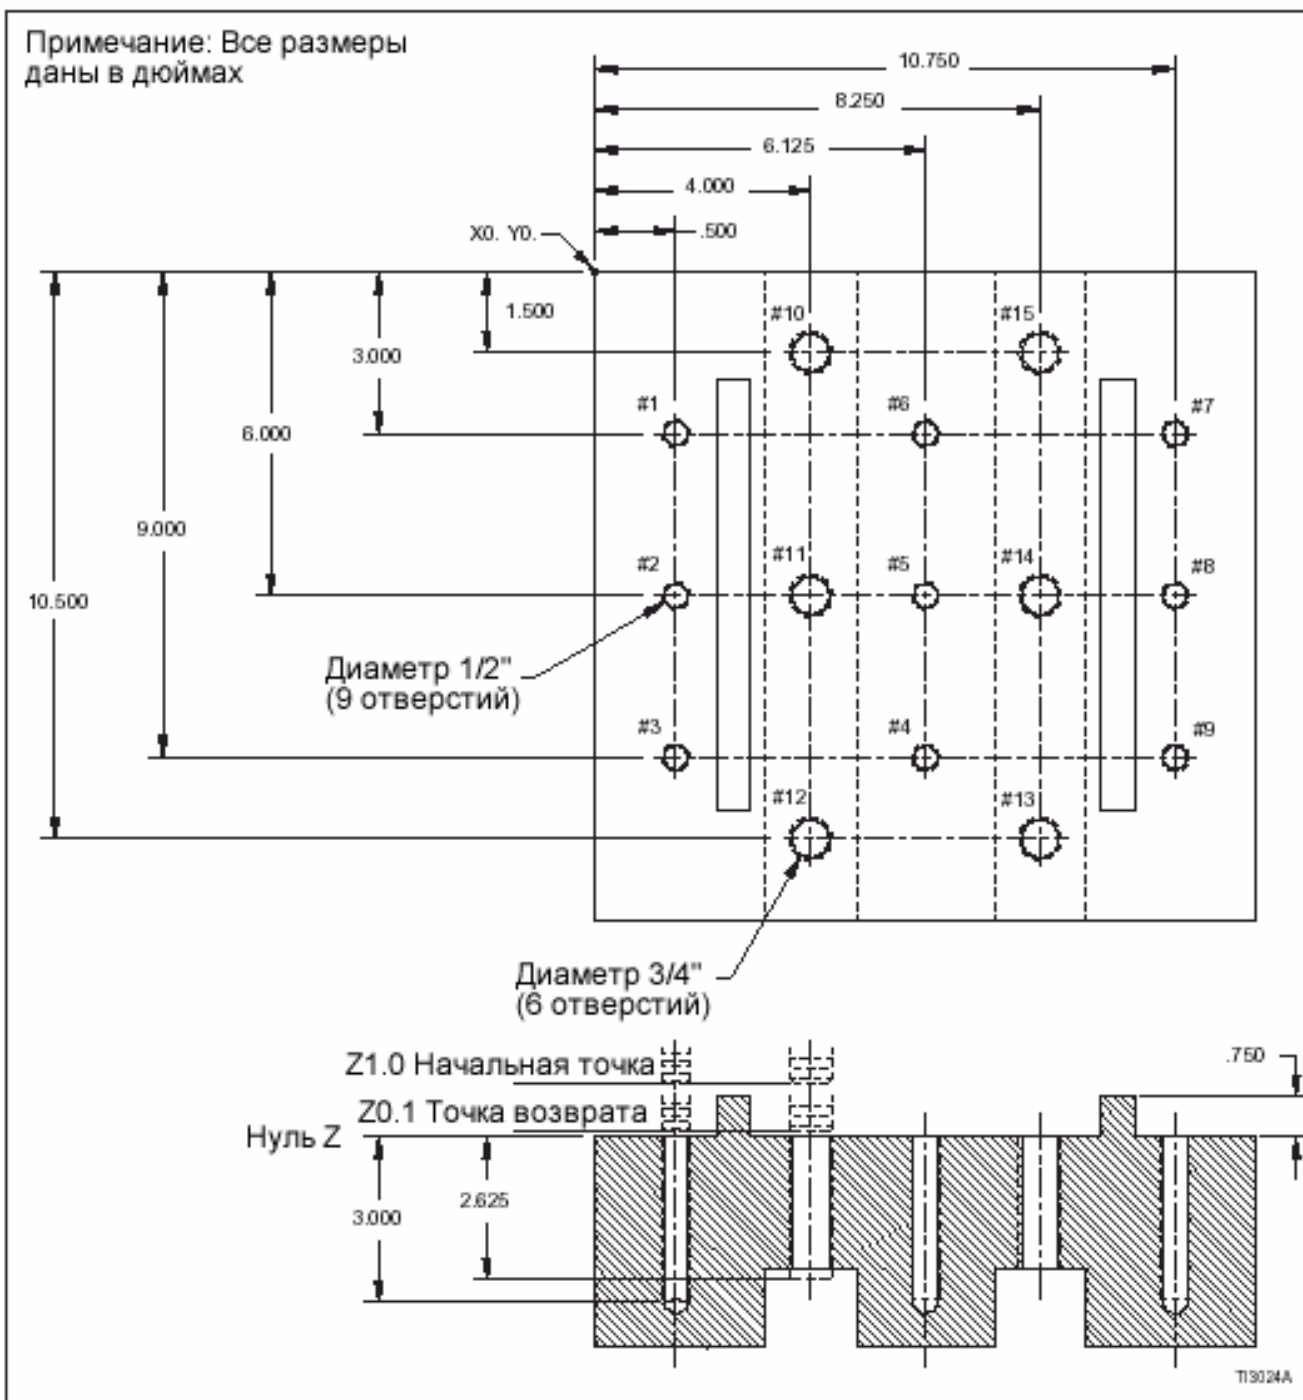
Типовая заготовка: нарезание нескольких резьбовых отверстий в циклах нарезания резьбы метчиком.
